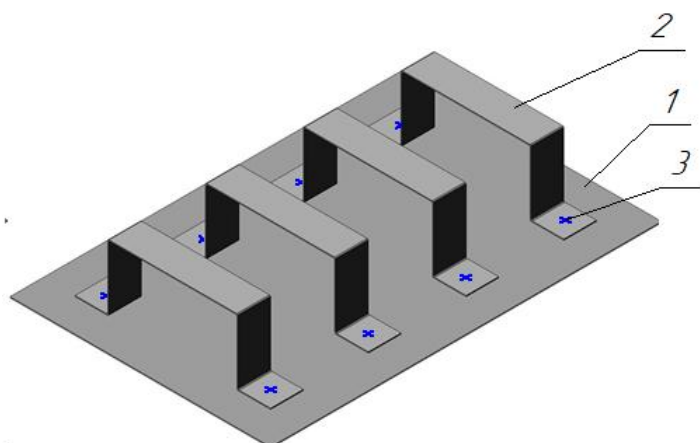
Кронштейн: 1 – пластина, 2 – скоба, 3 – сварочные точки
